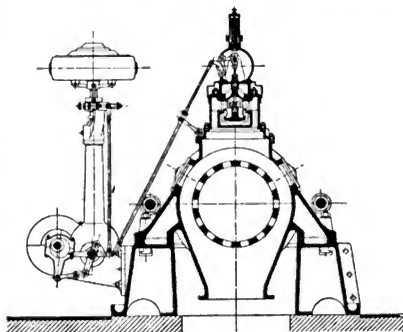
Zwangsläufig gesteuertes Rücklaufventil, Patent König der Ascherslebener Maschinenbau-Aktiengesellschaft.
